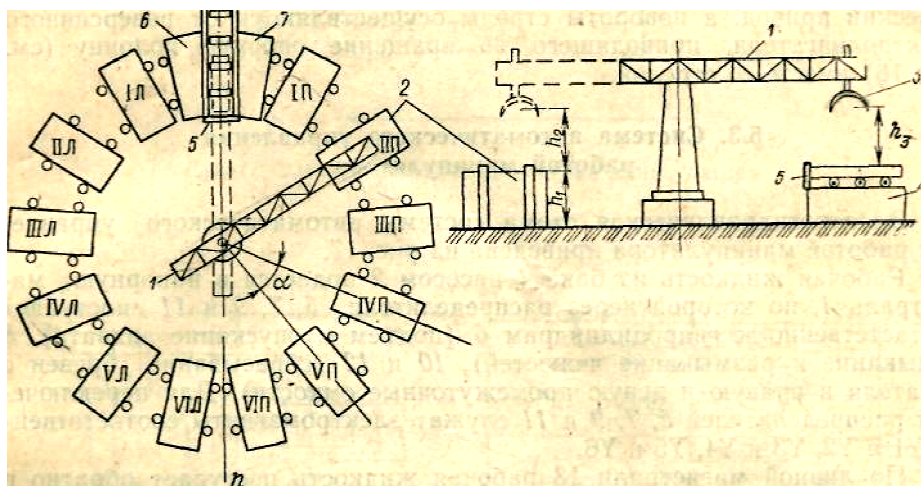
Схема сортировочно-пакетирующего участка с манипулятором
